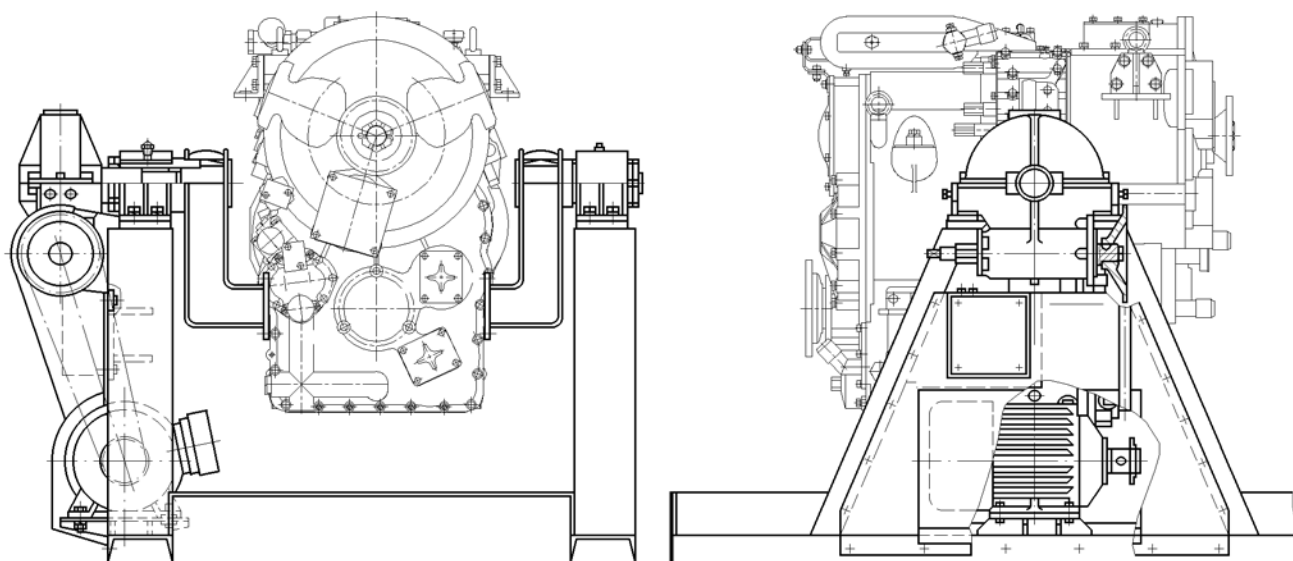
Стенд для разборки и сборки гидромеханической передачи
